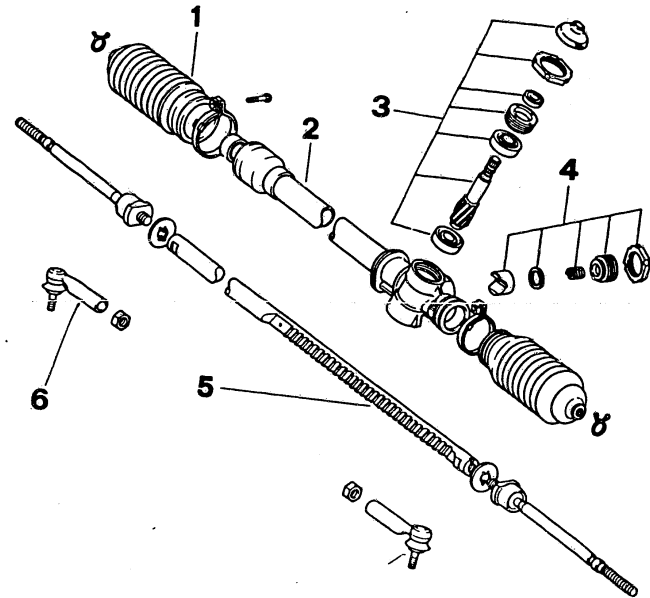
Einzelteile des Lenkgetriebes: 1 Gummibalg – 2 Lenkgehäuse – 3 Ritzel mit Lagerung – 4 Andrückkölbchen mit Feder und Einstellschraube – 5 Zahnstange – 6 Spurstangengelenk.
